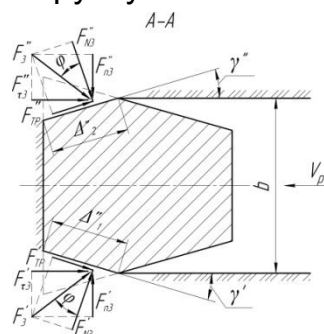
Схема взаємодії ґрунту з різцем на площадках зносу бокових граней
